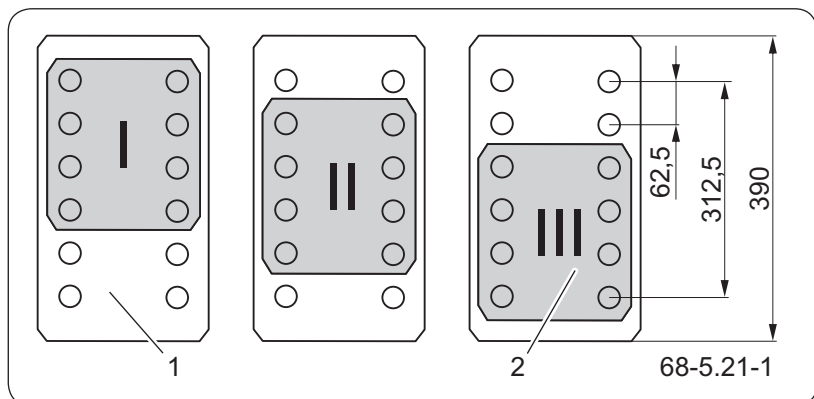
Abmessungen der Frontplatte des Rahmens
